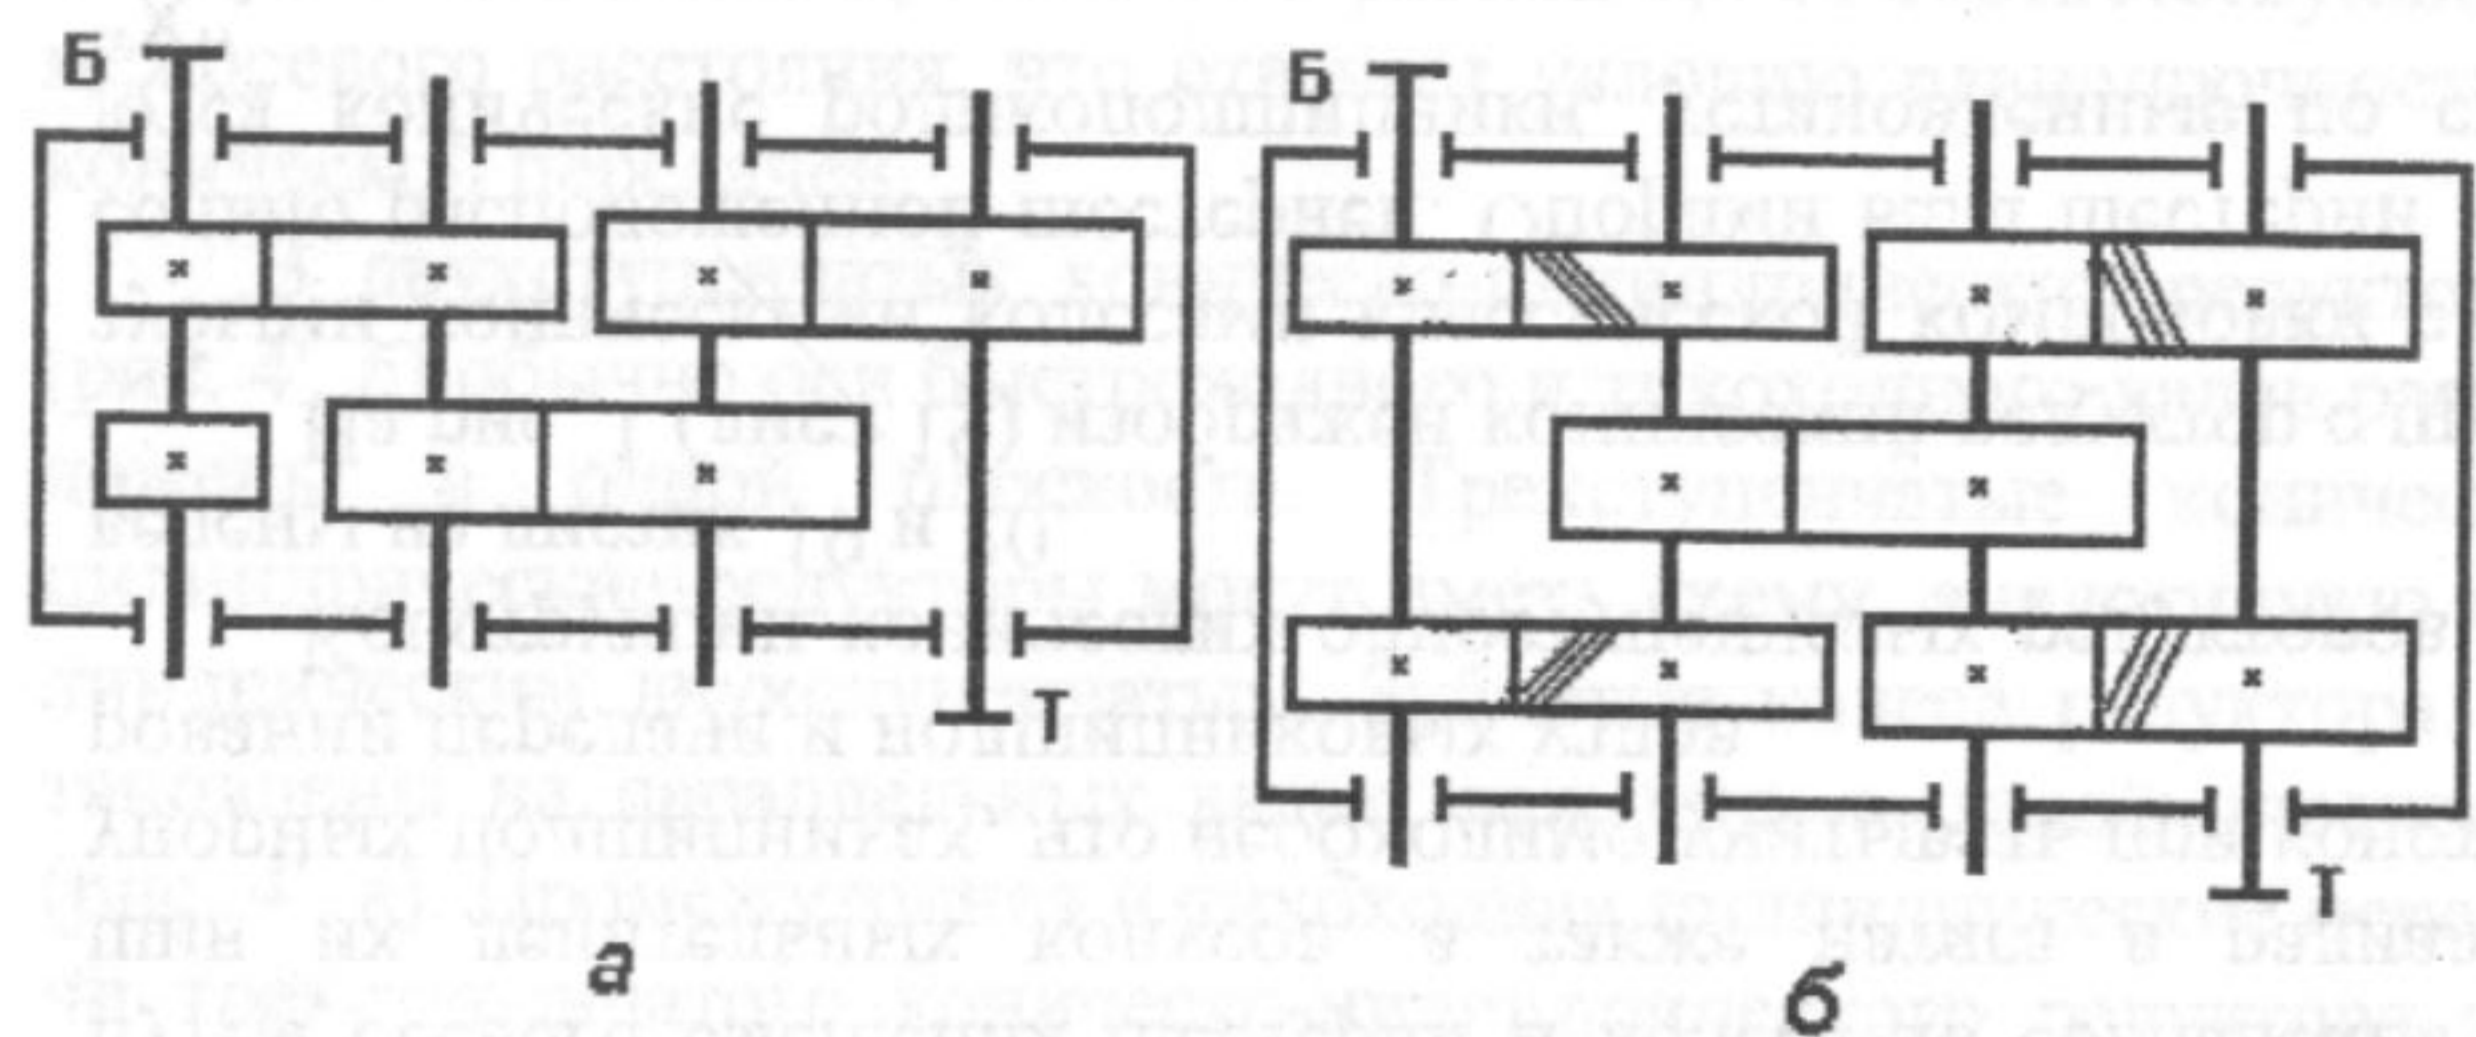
'. Кинематические схемы цилиндрических трехступенчатых редукторов
